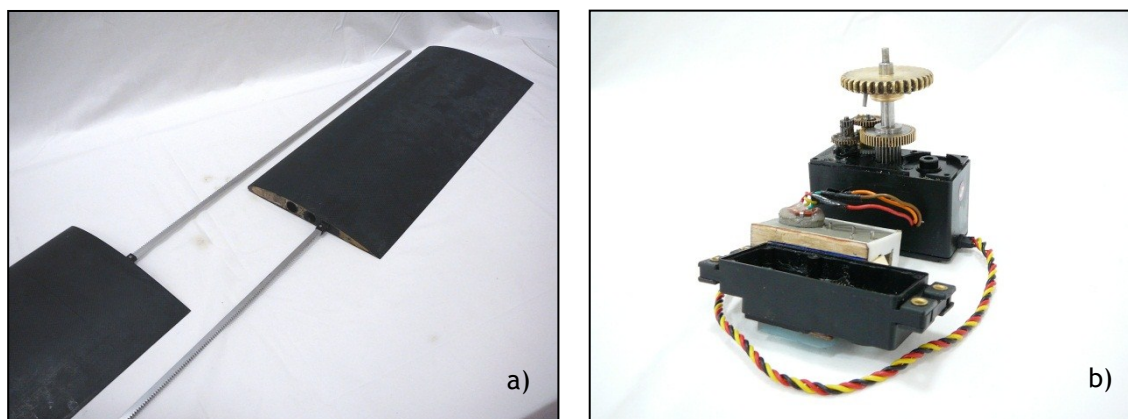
Aperfeiçoamento do mecanismo de engrenagem: a) cremalheiras, b) conjunto servo-motor.
